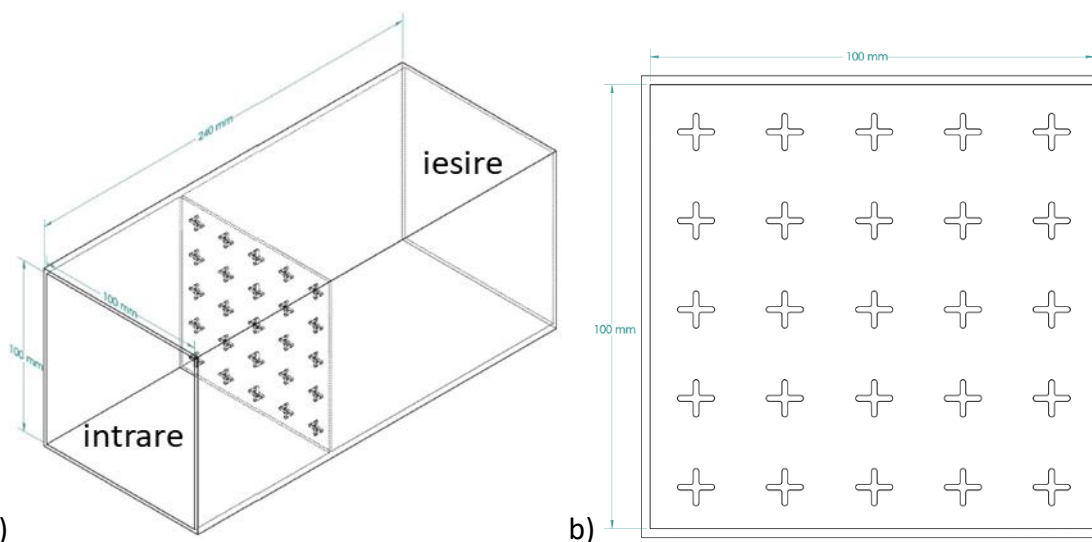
Construcție geometrie grilă cu 25 de orificii tip „+” - a) vedere izometrică, b) vedere frontală
